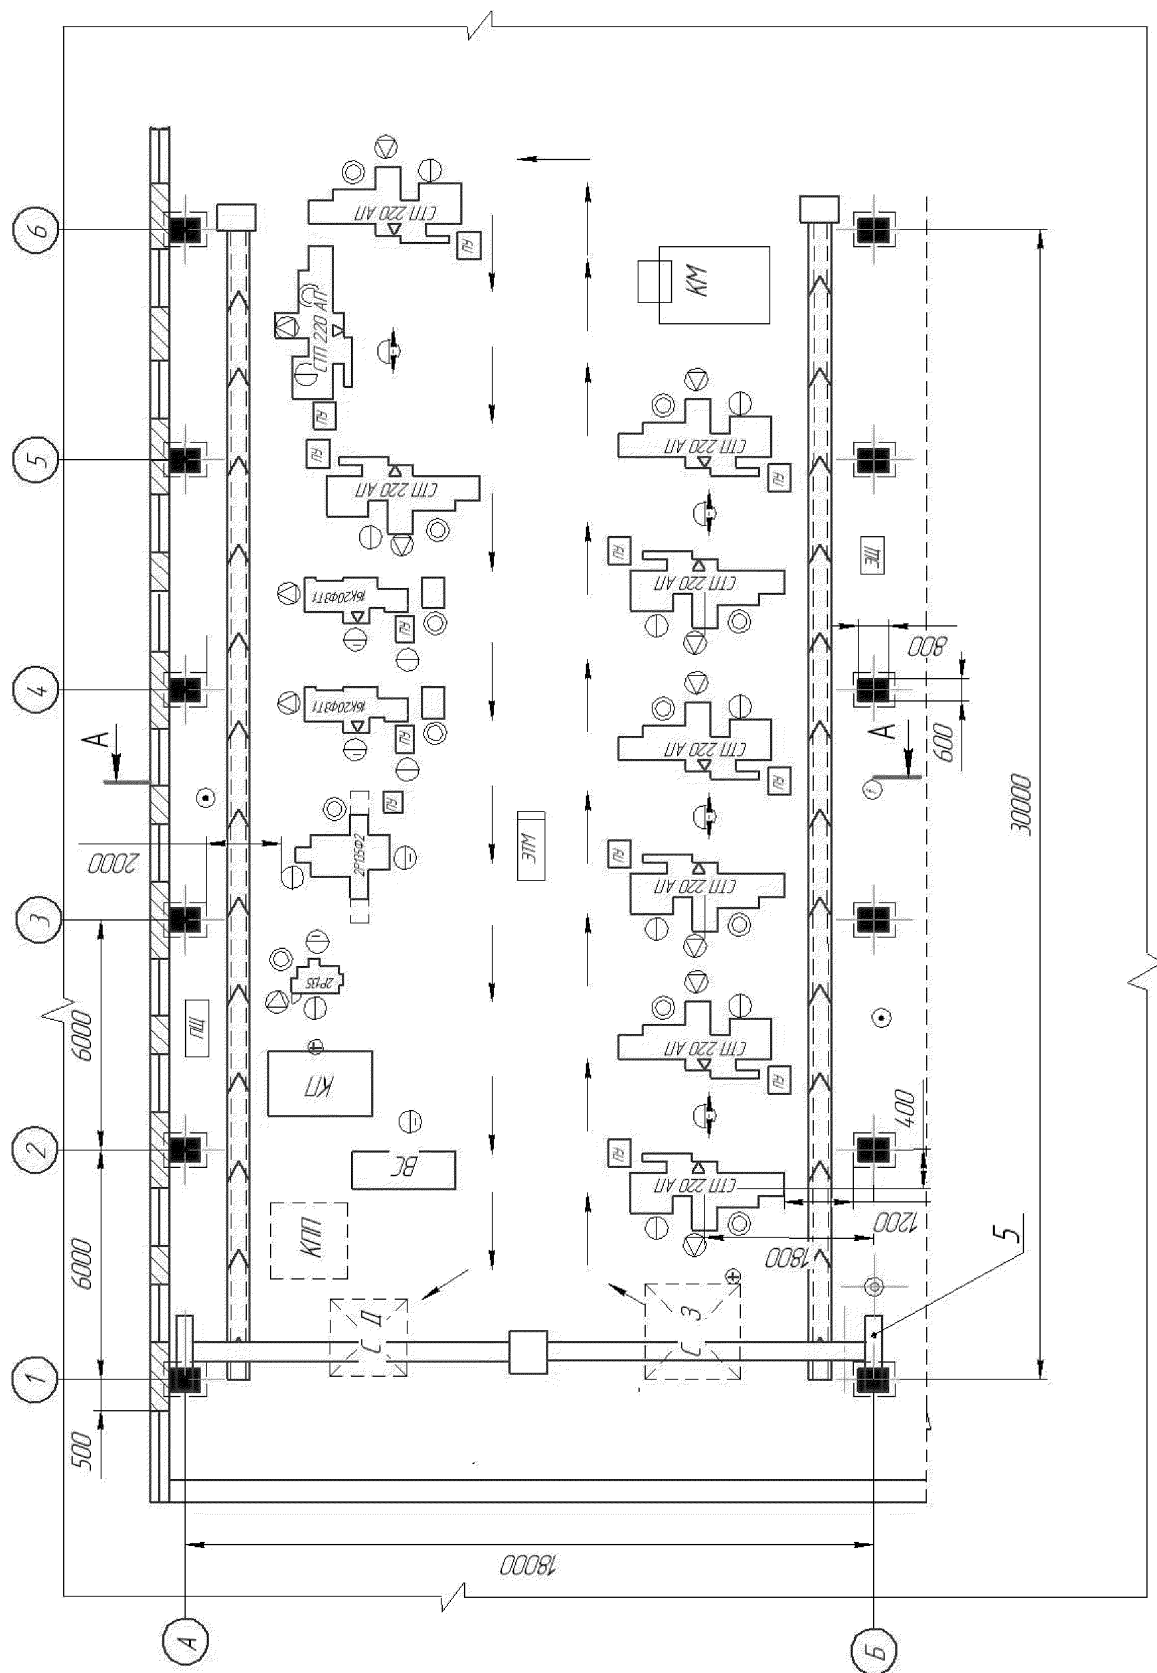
Планировка участка механической обработки Детали «Полумуфта»
